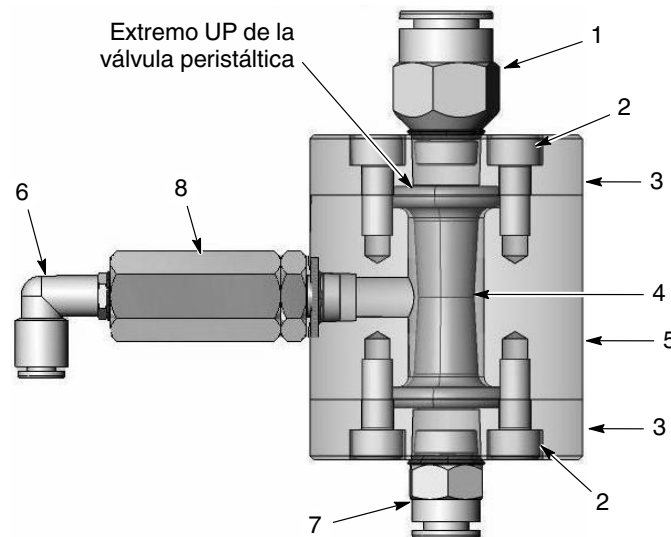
Vista de la sección transversal de la válvula de descarga
